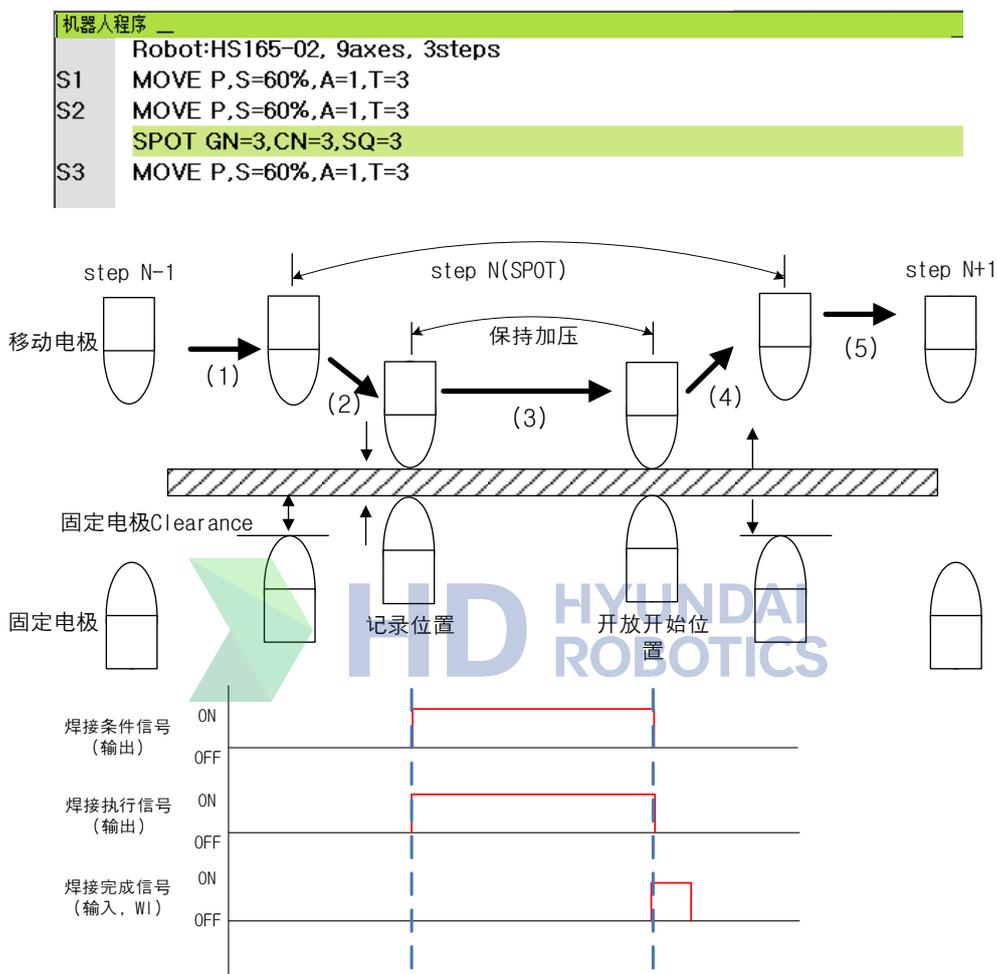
Eqlless 焊接枪点焊的再现
